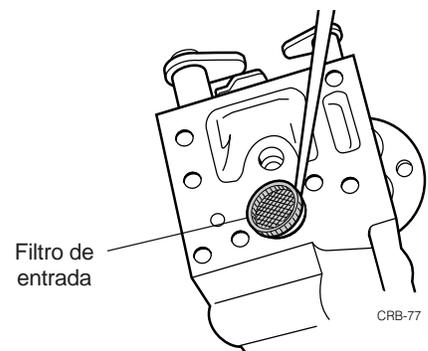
Como sacar el filtro de entrada (Carburador HDA)
